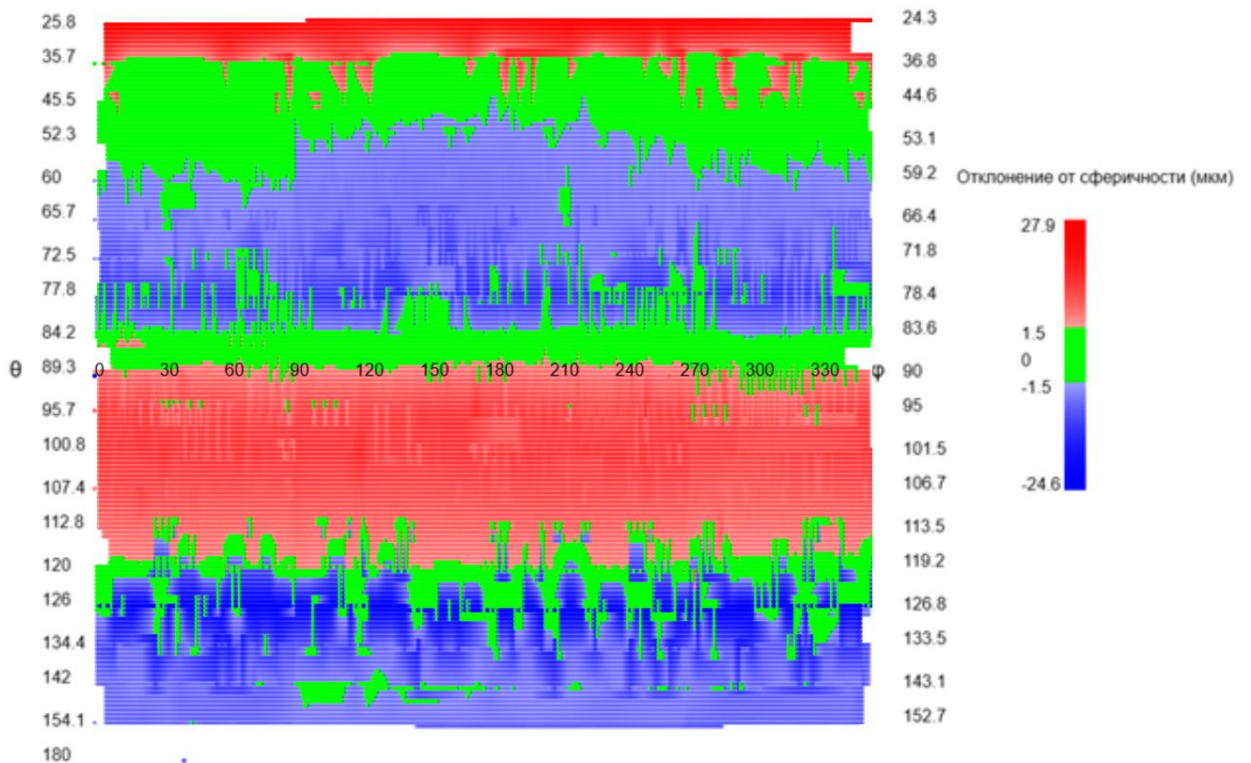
Развертка сферической поверхности шарового пальца №5 после притирки
